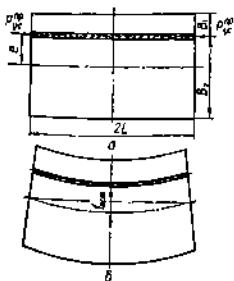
Деформации изгиба при сварке *встык* пластин различной ширины
